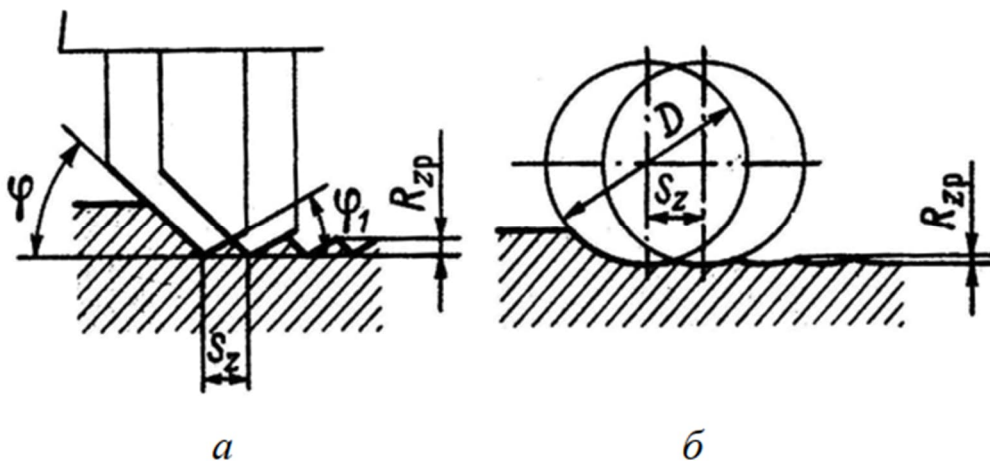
Розрахунковий мікропрофіль обробленої поверхні при фрезеруванні торцевою (а) та циліндричною (б) фрезами
